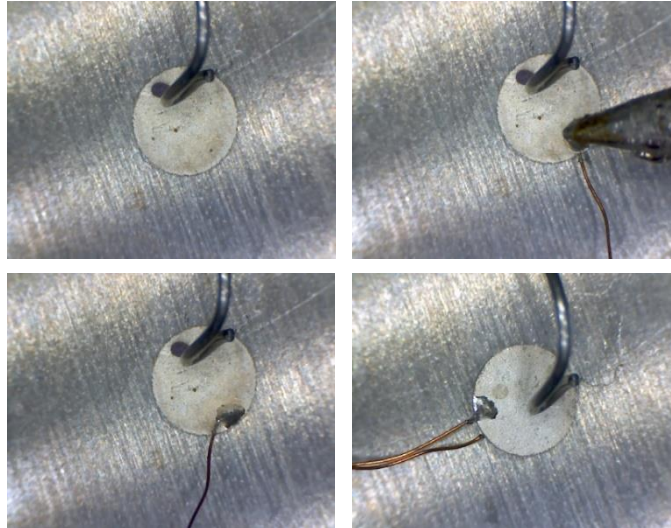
Soldadura do piezoelétrico a) piezoelétrico b) momento da soldadura c) lado 1 d) lado 2
